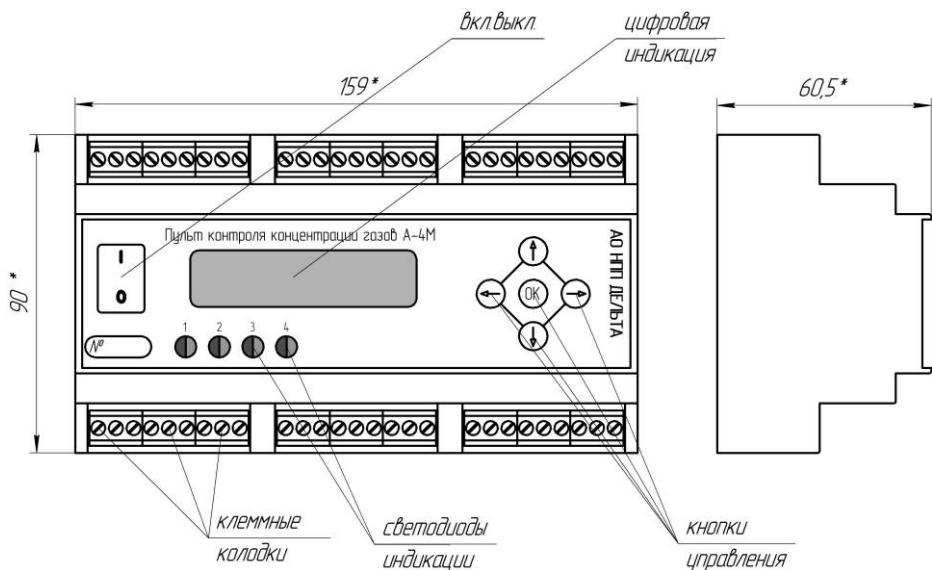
Внешний вид и габаритные размеры пульта контроля А-4М
